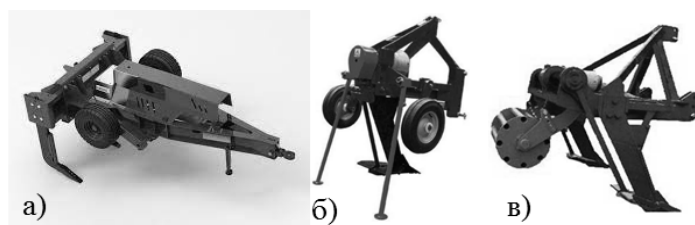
Глубокорыхлители с активными вибрирующими рабочими органами: а — VT/TA *Vibrasoil*; б — GP-1-60; в — GP-2-60
